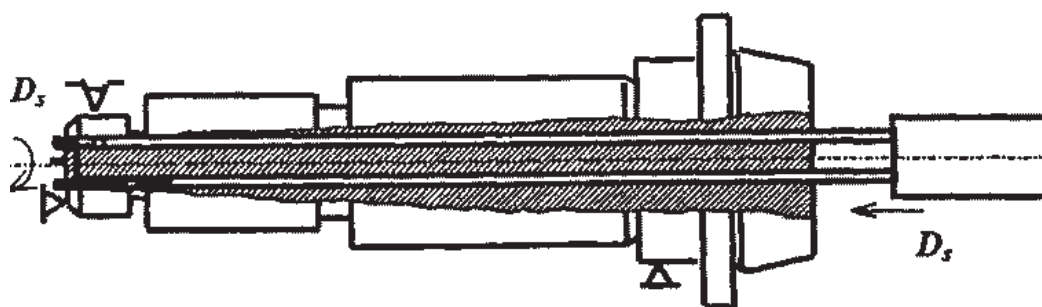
Схема обработки центрального отверстия кольцевым сверлом
